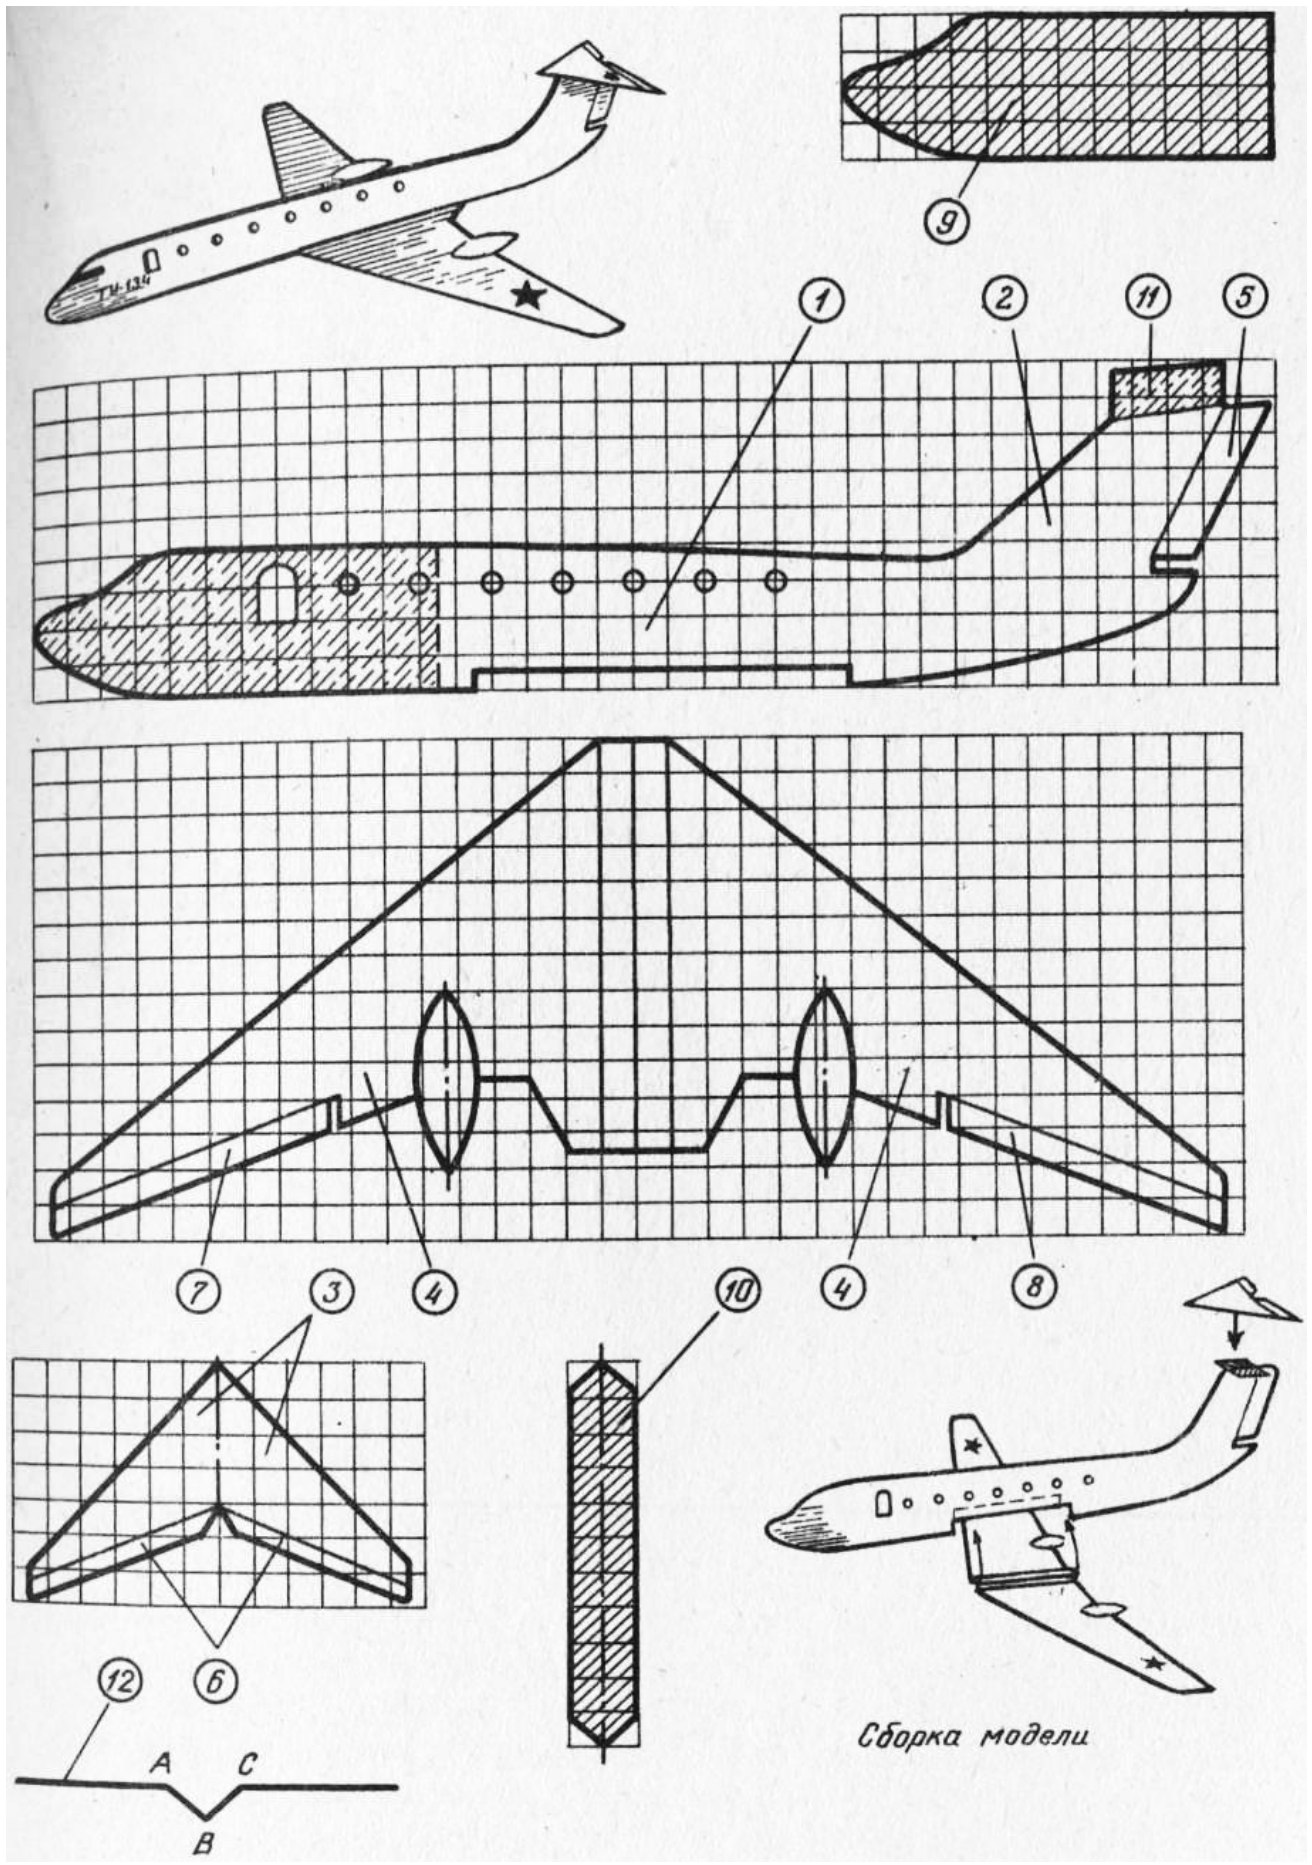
Модель самолета Ту-134: 1 — фюзеляж; 2 — киль; 3 — стабилизаторы; 4 — крылья; 5 — руль поворота; 6 — руль высоты; 7 — элерон левый; 8 — элерон
